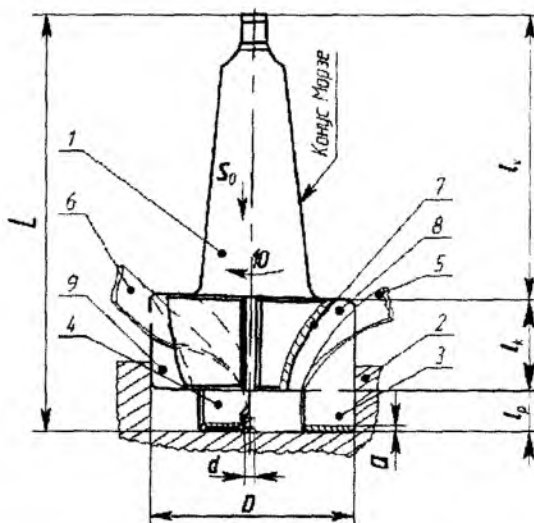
Конструкция режущей головки: 1 – режущая головка; 2 – заготовка; 3 – резец, расположенный у периферии режущей головки (внешний резец); 4 – резец, расположенный у оси режущей головки (внутренний резец); 5 – срезаемая внешним резцом стружка ( $a$  – толщина среза); 6 – срезаемая внутренним резцом стружка; 7 – грязевая канавка (условно совмещена на чертеже с осью режущей головки); 8 – стружечная канавка у внешнего резца; 9 – стружечная канавка у внутреннего резца; 10 – вращательное движение режущей головки при точении отверстия;  $S_0$  – осевая подача;  $D$  – диаметр отверстия;  $d$  – диаметр стержня, остающийся вдоль оси заготовки, периодически обламывающегося и уносящегося стружкой;  $l_k$  – длина корпуса режущей головки;  $l_p$  – вылет (высота) резца;  $l_x$  – длина хвостовика;  $L$  – длина режущей головки; А-А – сечение для идентификации геометрии резца в плоскости, касательной к траектории выбранной точки режущей кромки резца; Б-Б – сечение резцов для идентификации их геометрии в плоскости, перпендикулярной оси режущей головки
